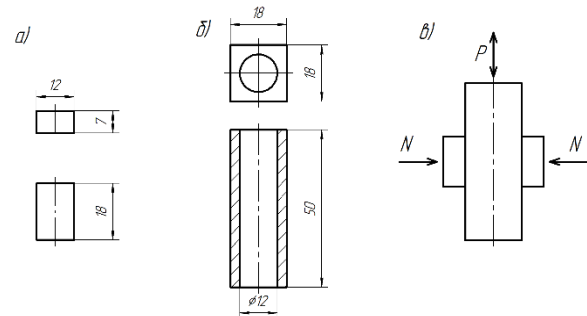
а – неподвижный образец, б – подвижный образец, в – схема нагружения.
